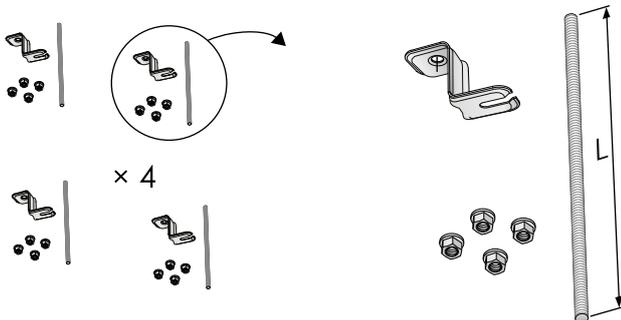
Montageteil SYST MS M8-1, Deckenbefestigung und Gewindestange
